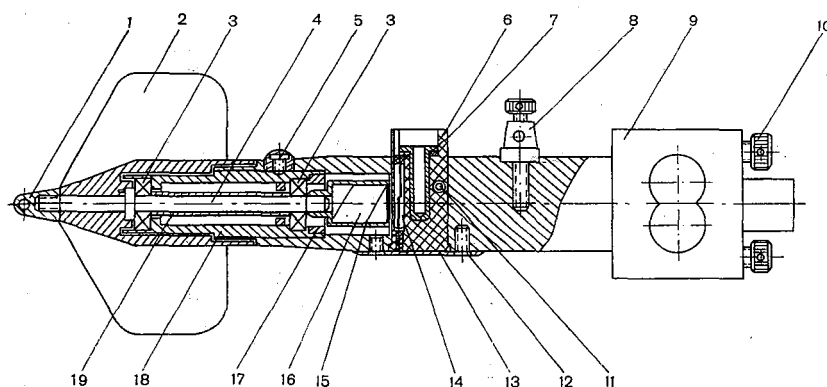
Устройство гидрометрической вертушки ГР-99.
